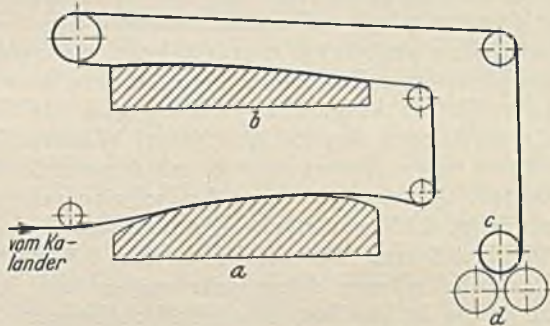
Einrichtung zum Pudern und Aufwickeln dünner Platten
